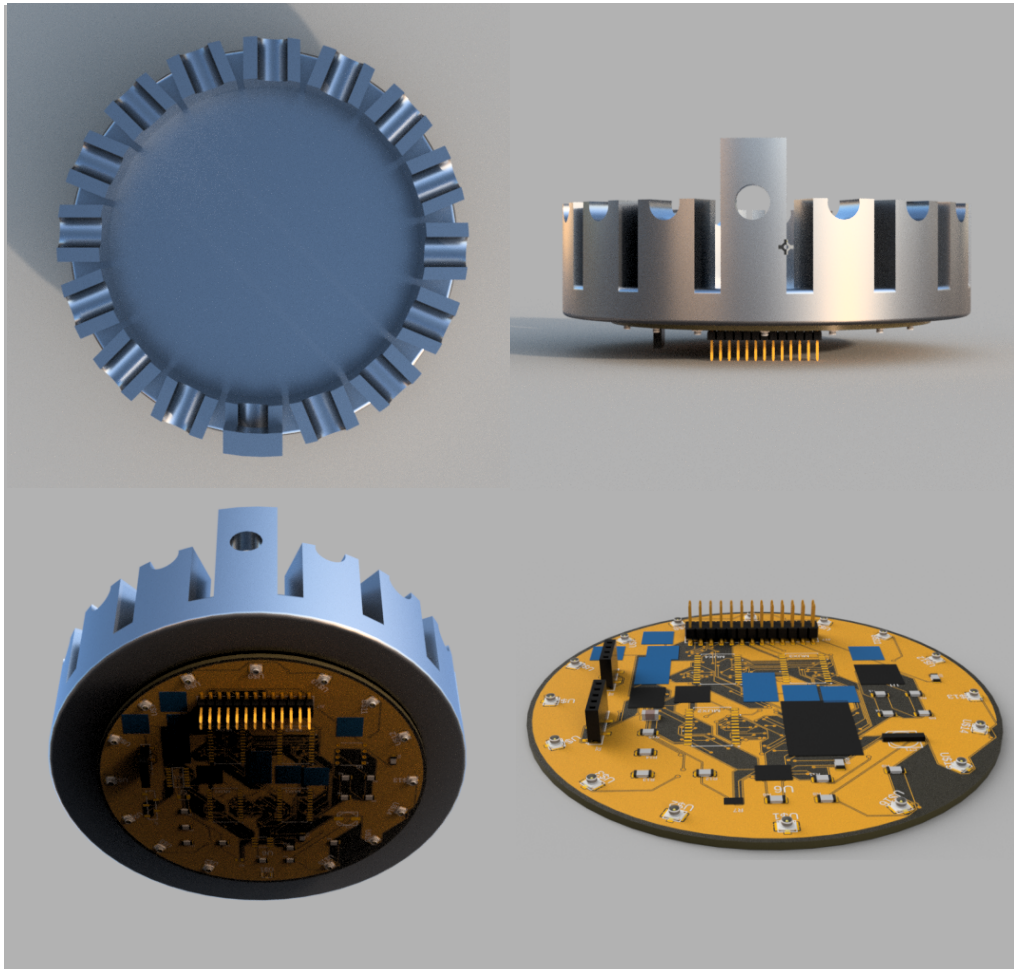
La base del tanque y la placa de circuitos impresos (PCB) se ha diseñado en Fusion 360. Se conservan los valores de elementos en el diseño del circuito.
